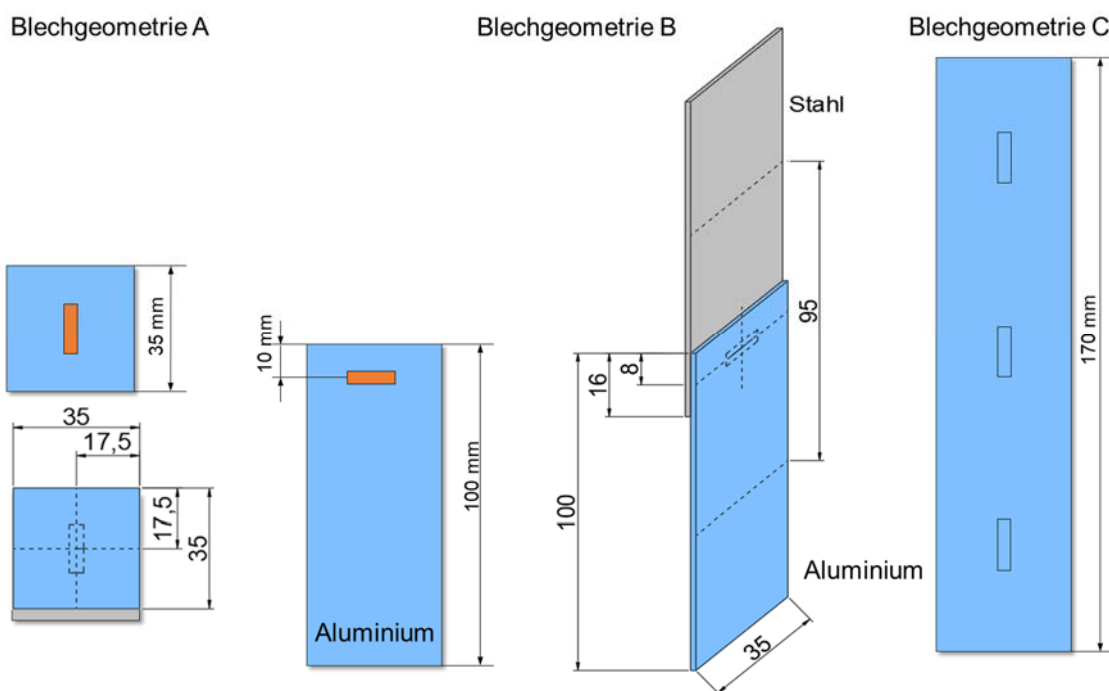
Technische Zeichnungen der verwendeten Schweißprobengeometrien
